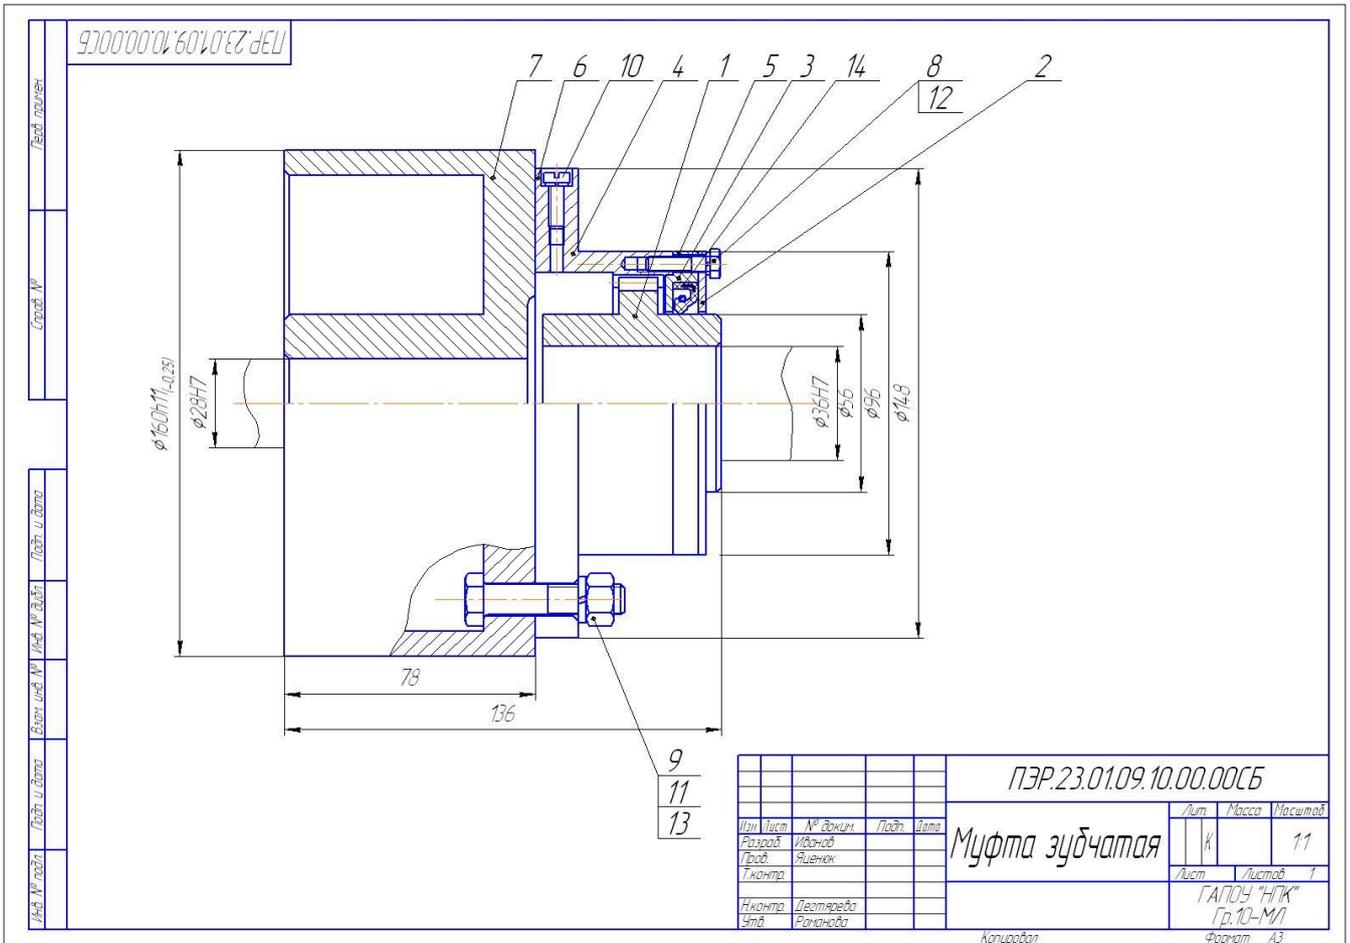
Сборочный чертёж «Муфты зубчатой»
